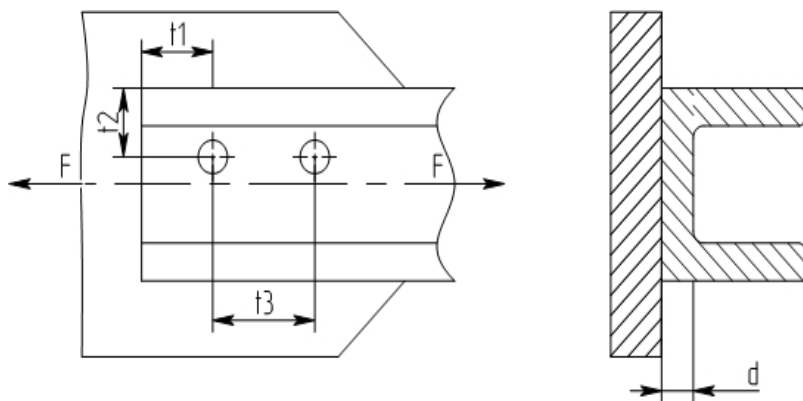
Швеллер, приваренный к косынке точечной сваркой
